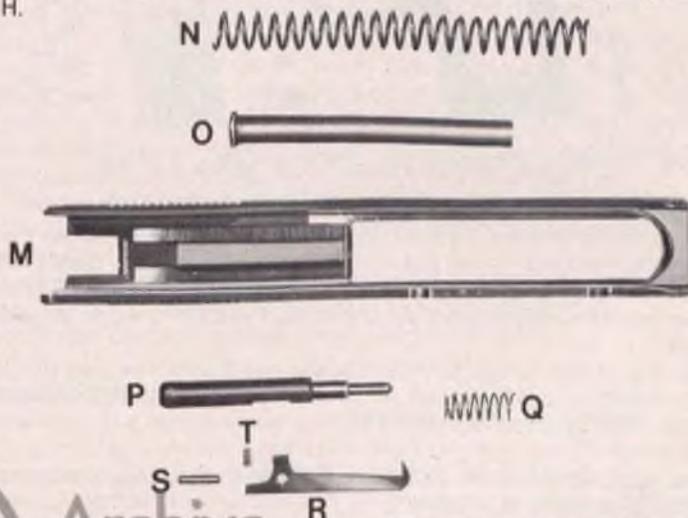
Einzelteile des Verschlusses: M = Verschlußstück, N = Schließfeder, O = Druckbolzen, P = Schlagstift, Q = Schlagstiftfeder, R = Auszieher, S = Auszieherstift, T = Auszieherfeder.
